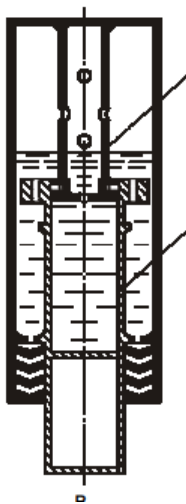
схема плунжерного однокамерного амортизатора
